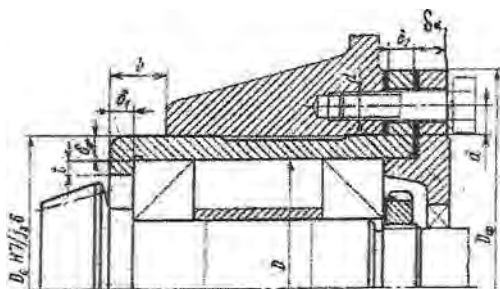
Конструкция стакана для фиксирующих опор или опор конических зубчатых колес.
